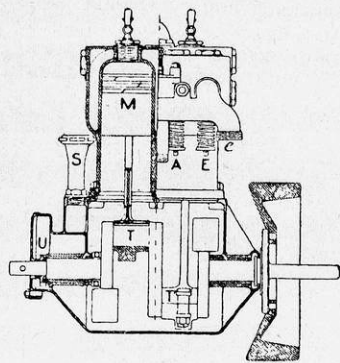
Двухцилиндровый двигатель съ колѣнчатымъ валомъ, лежащимъ въ двухъ подшипникахъ.
